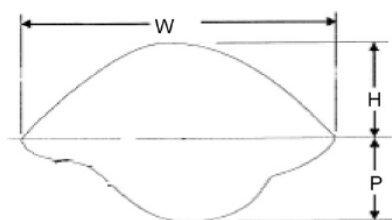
Parâmetros geométricos do cordão de solda.
